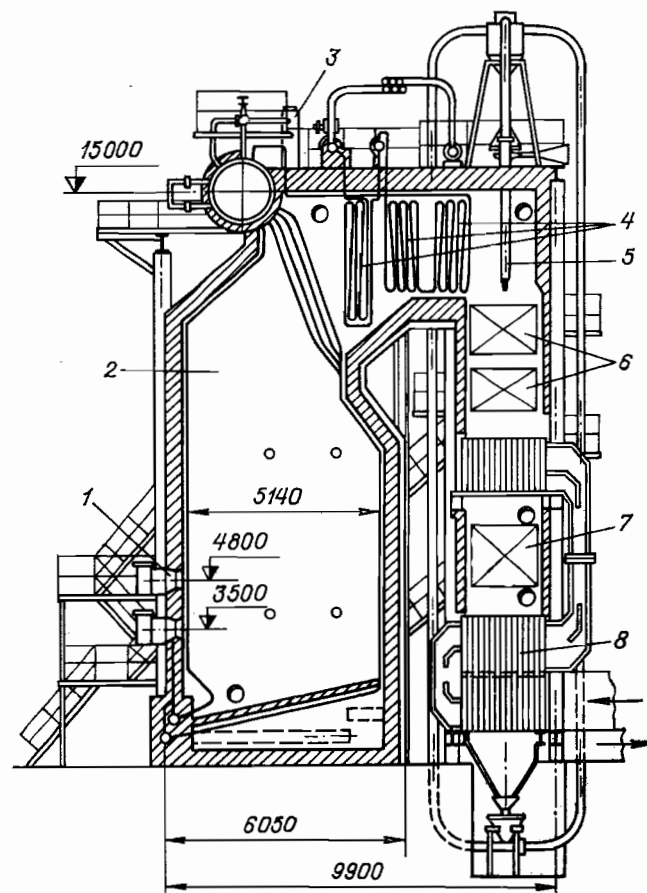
Газомазутный котлоагрегат БКЗ-75-39ГМА [24].
